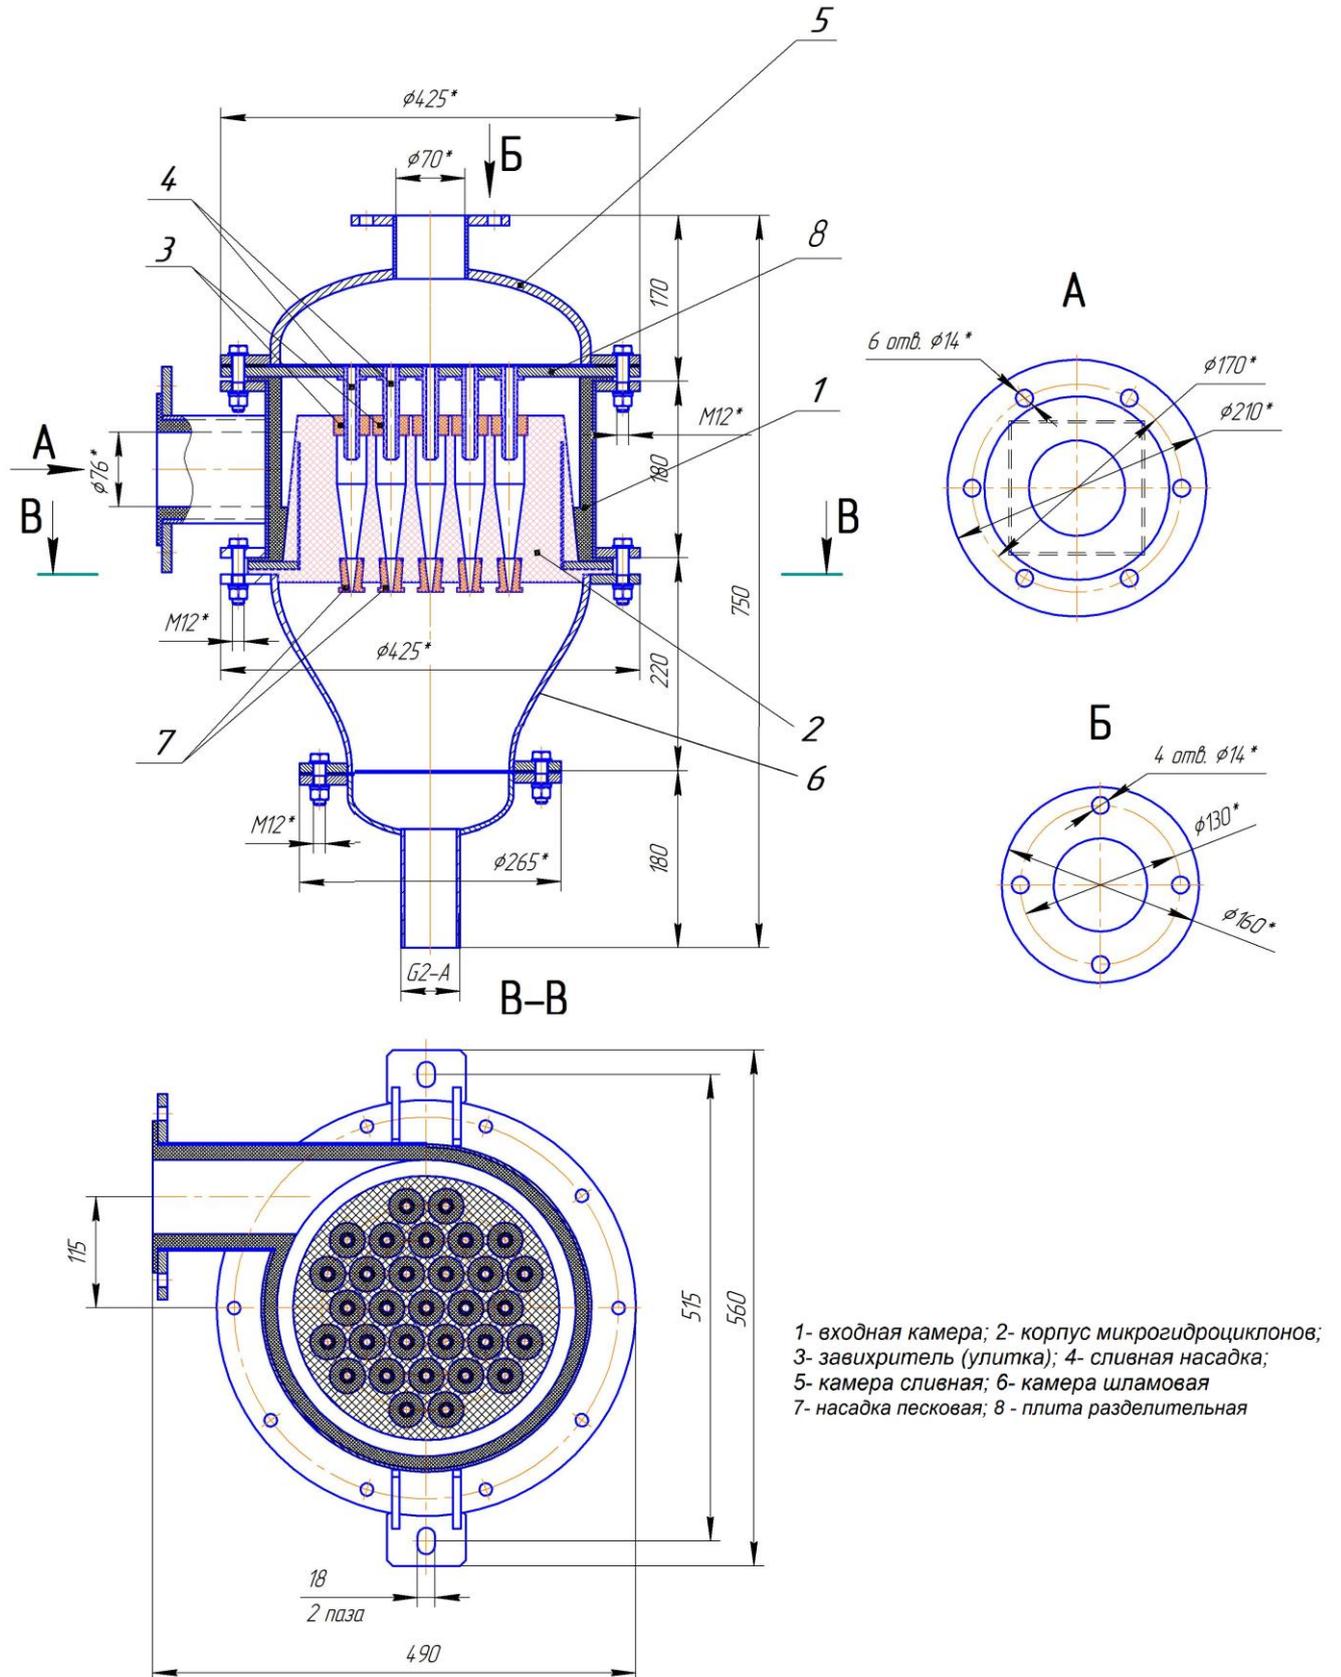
Габаритные и присоединительные размеры фильтра МГЦ
